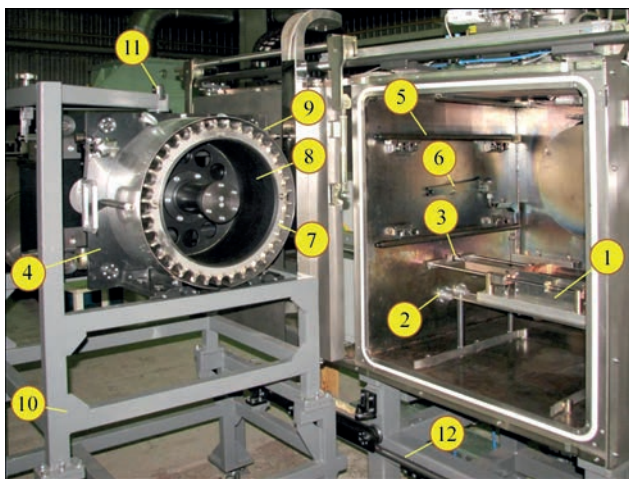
Загальний вигляд більшості механізмів, що пов'язані з ЕПО: 1 – механізм обертання деталей; 2 – привід цього механізму; 3 – механізм повздовжньої подачі деталей; 4 – барабанний магазин деталей; 5 – рейки підвіски магазину в камері; 6 – привід магазину; 7 – змінний вкладиш з комірками для деталей; 8 – поворотний барабан магазину; 9 – зовнішня обичайка магазину; 10 – рама завантажувального пристрою; 11 – поворотний вузол підвіски для двох барабанних магазинів цього пристрою; 12 – горизонтальна опорна рейка цього пристрою
